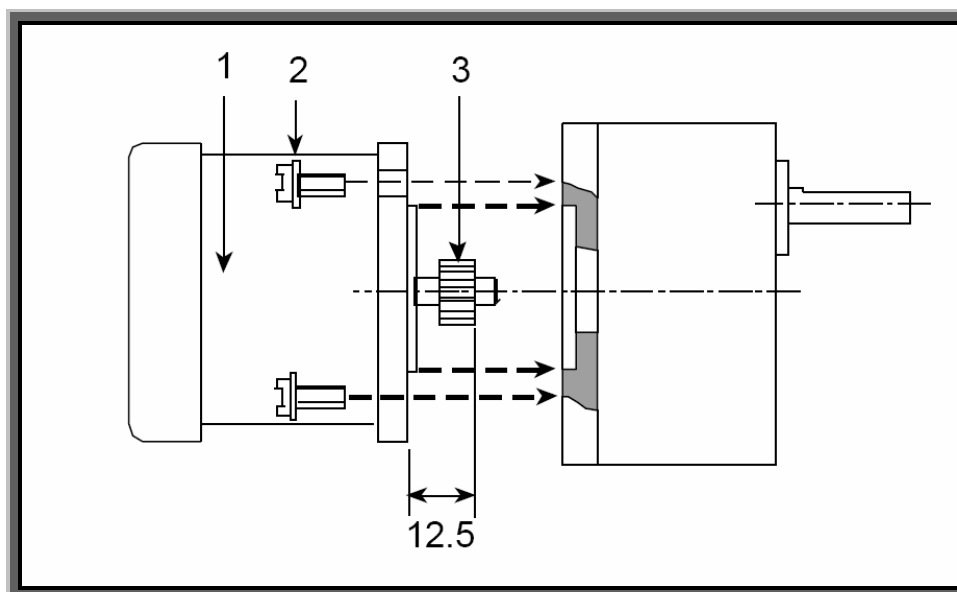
Posicionament del pinyó d'atac del motor per garantir el contacte. 1) motor.
